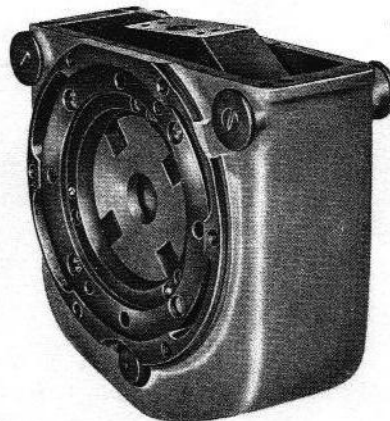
Radialkolbenpumpe Bauform B, Ausführung L
